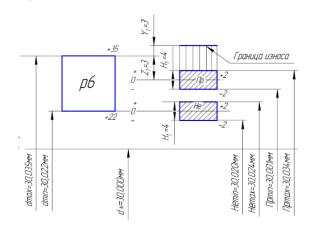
Схема расположения полей допусков калибров для контроля вала 30*p6
